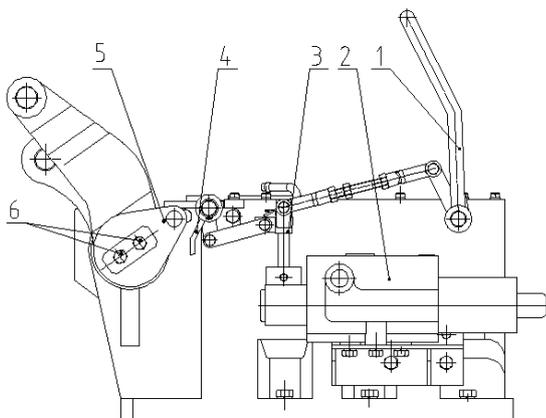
Регулировка высоты подъема гидравлической системы.
